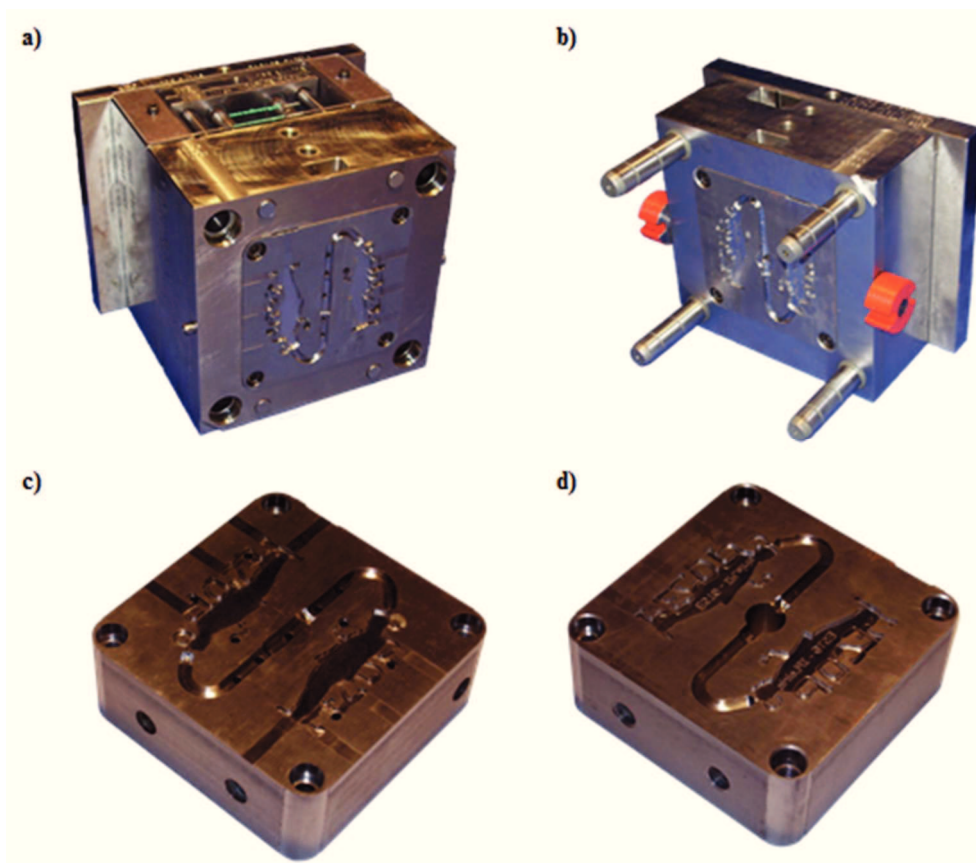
Molde com os elementos moldantes em aço montados na estrutura do molde de injeção: a) lado móvel; b) lado fixo; c) bucha do porta-chaves; d) cavidade do porta-chaves.
